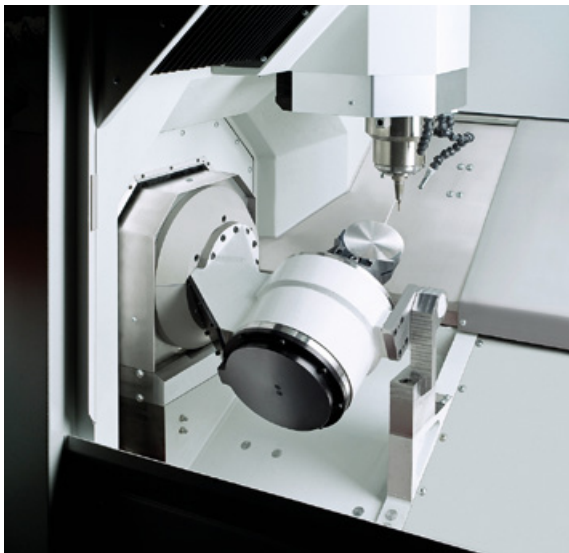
Bearbeitung auf einer 5-Achs-Maschine.
